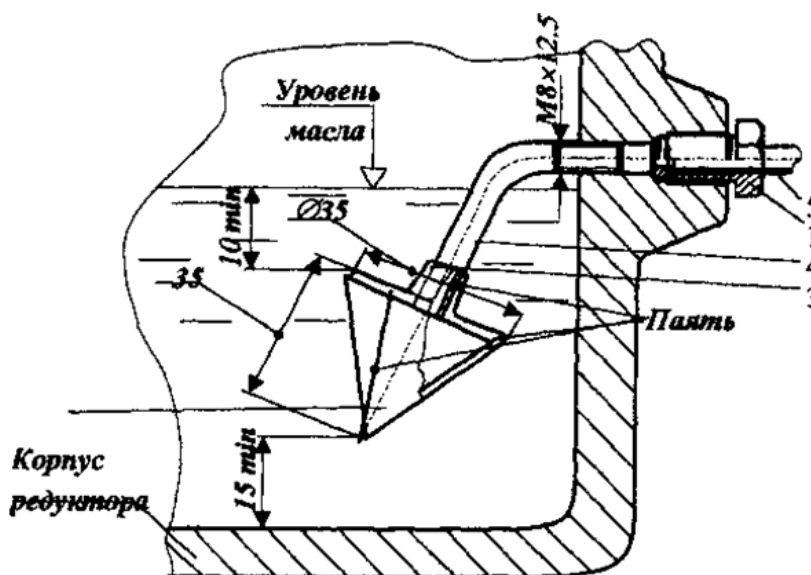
Конструкция заборного устройства для циркуляционной системы смазки: 1 – штуцер концевой; 2 – корпус заборника, сетка ; 3 – диск; 4 – труба; 5 – труба 8x10.
